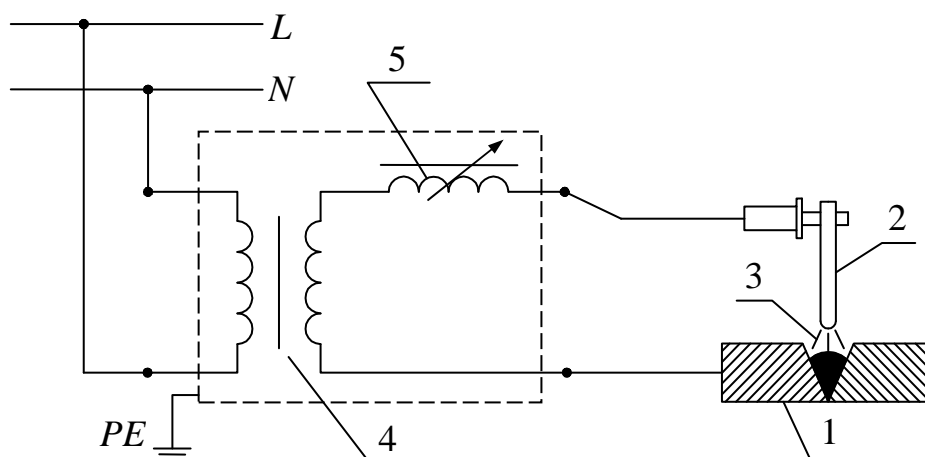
Принципиальная схема подключения сварочного трансформатора:
